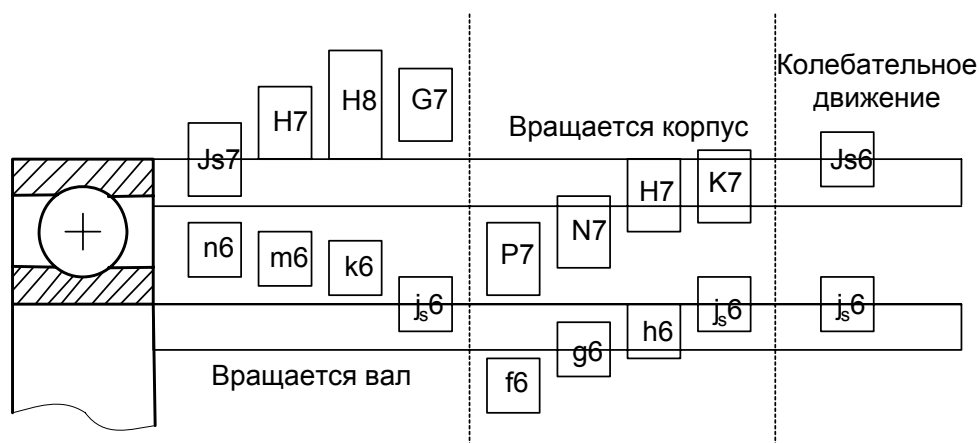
Поля допусков соединения деталей с подшипниками классов точности P0 и P6
